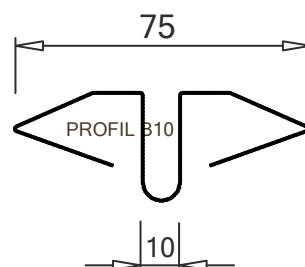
Géométrie des bardeaux et tolérances dimensionnelles
